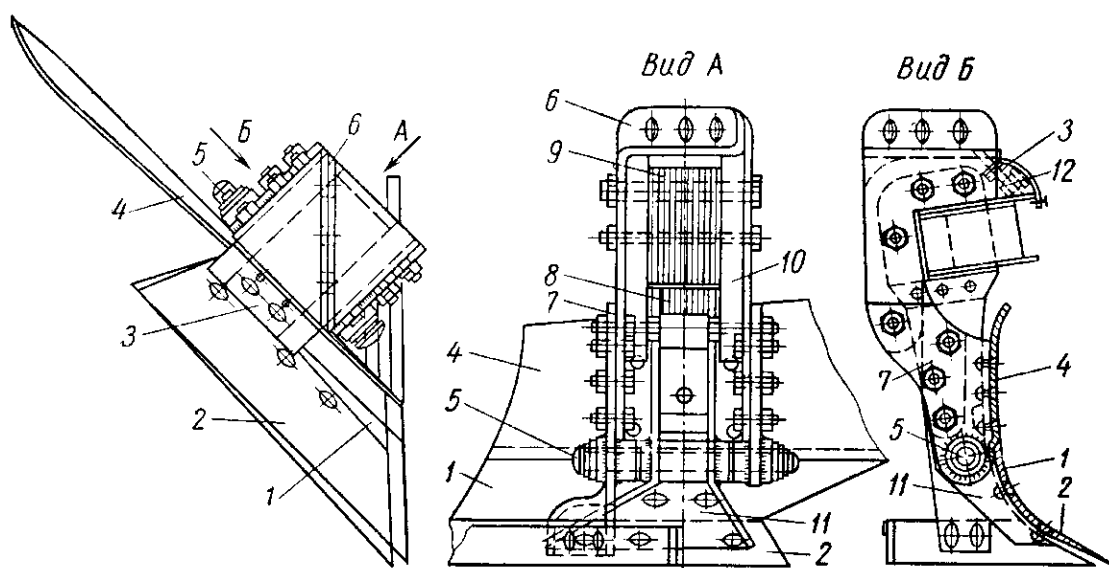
Вібраційний плужний корпус з електромагнітним вібратором.
